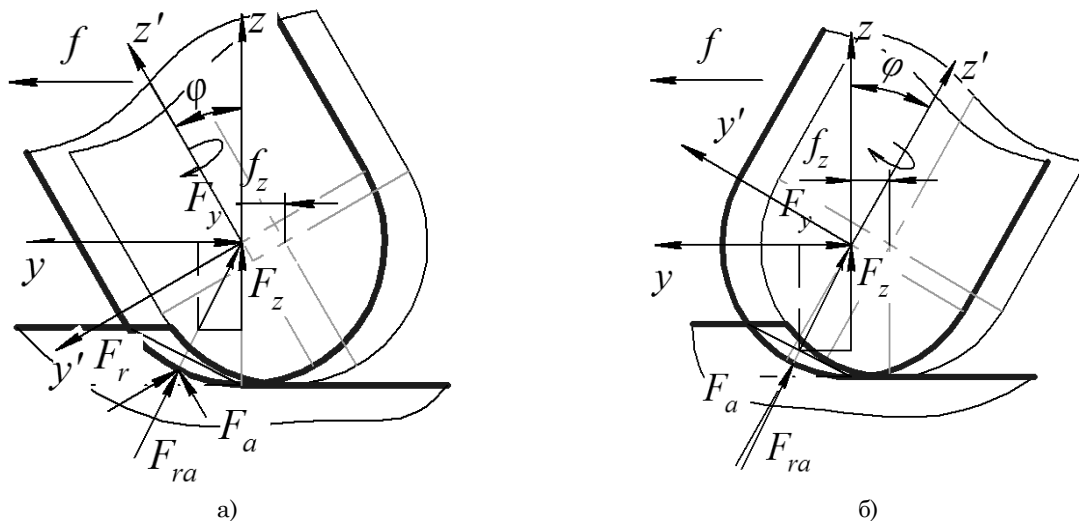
Схема шару, що зрізується, при фрезеруванні сферичними фрезами
